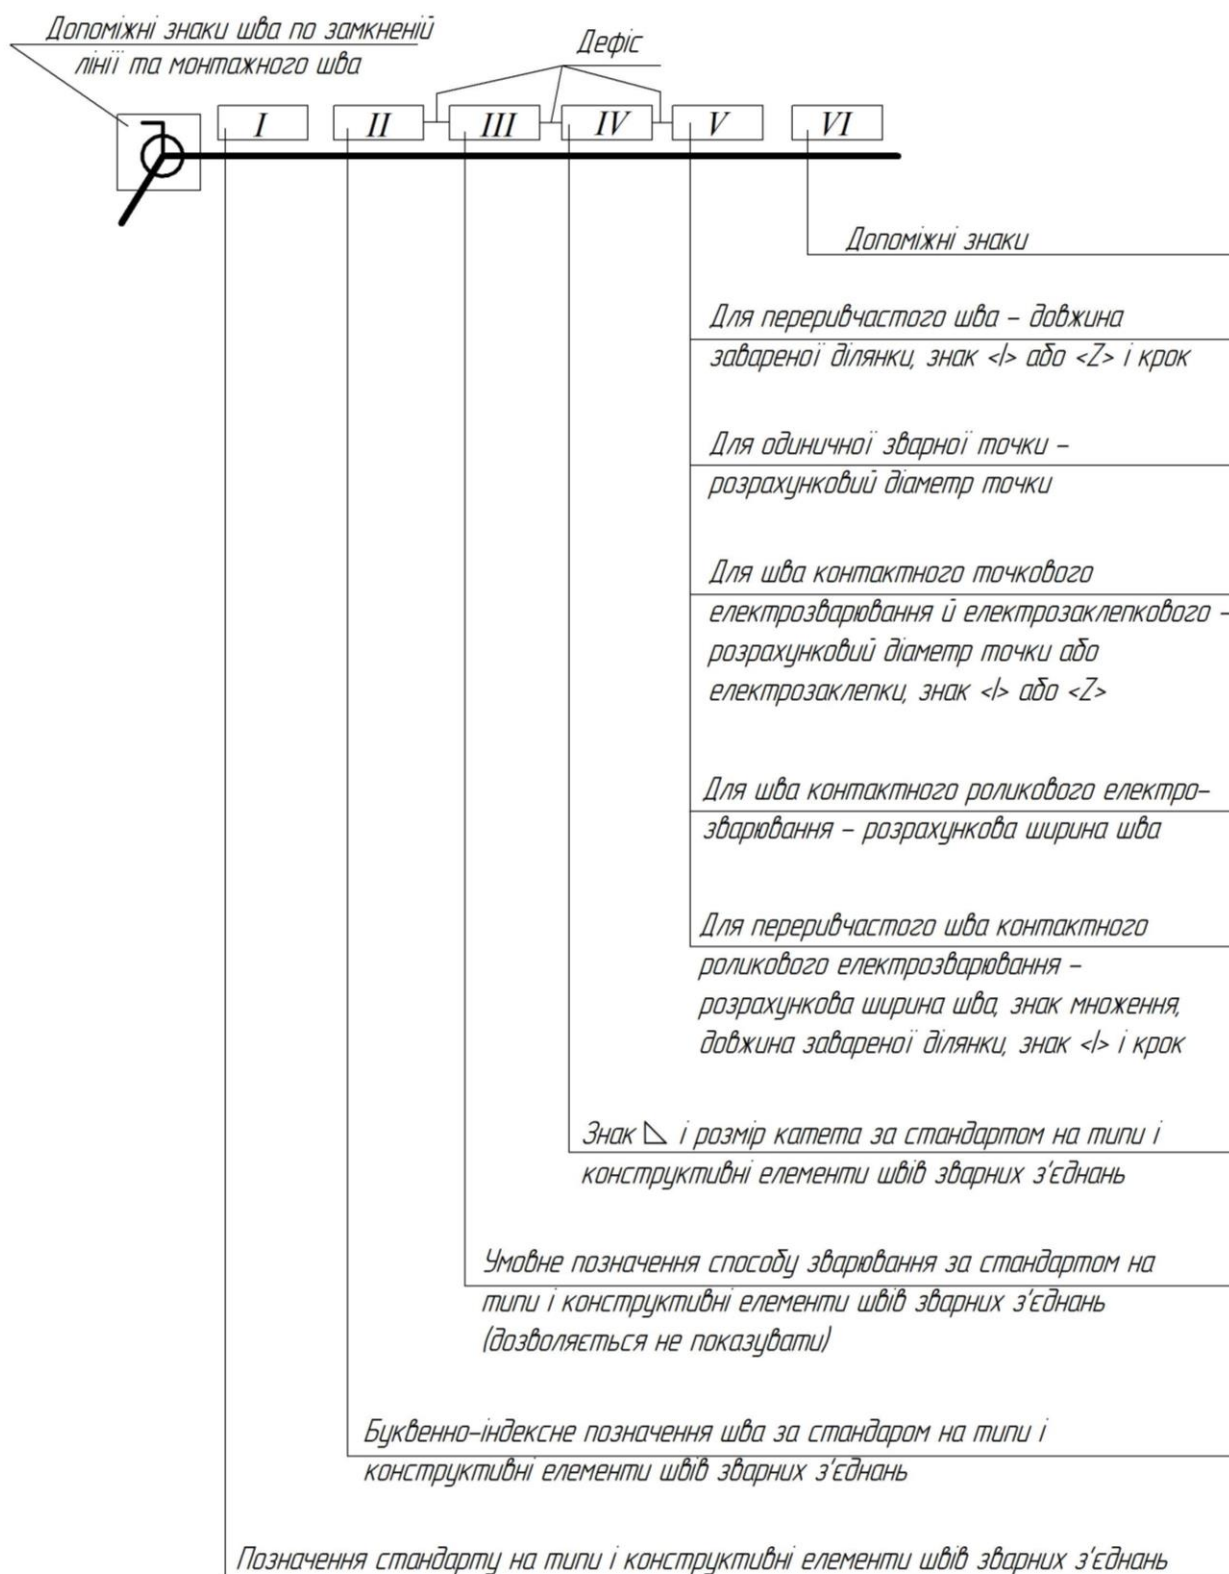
Схема умовного позначення стандартного шва або зварної точки
